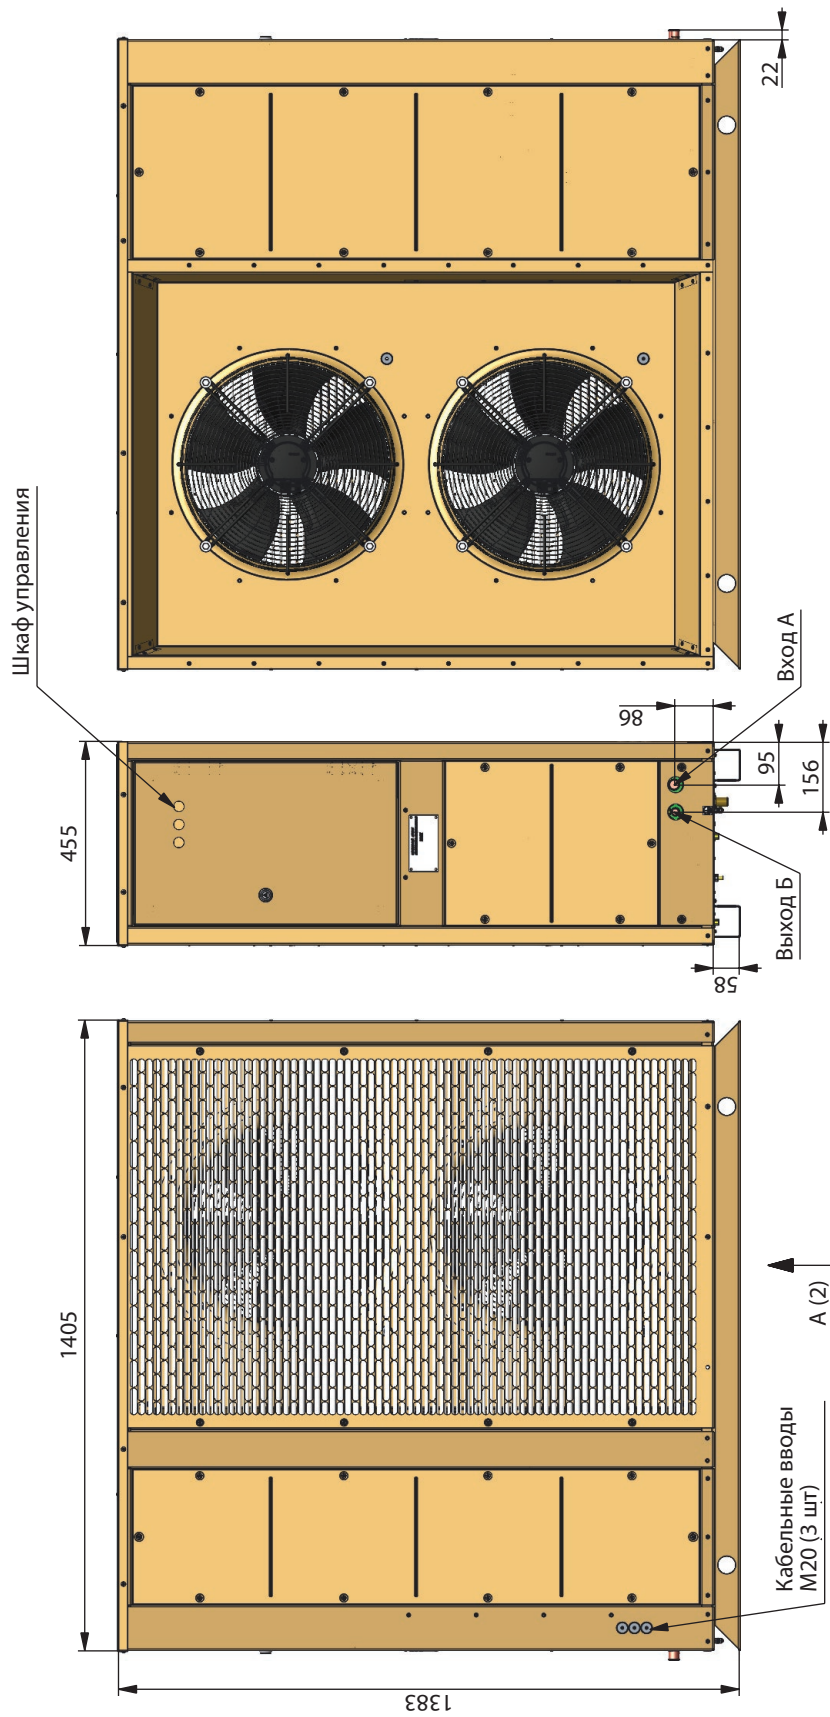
Агрегат компрессорный типа МАКК 110-201
